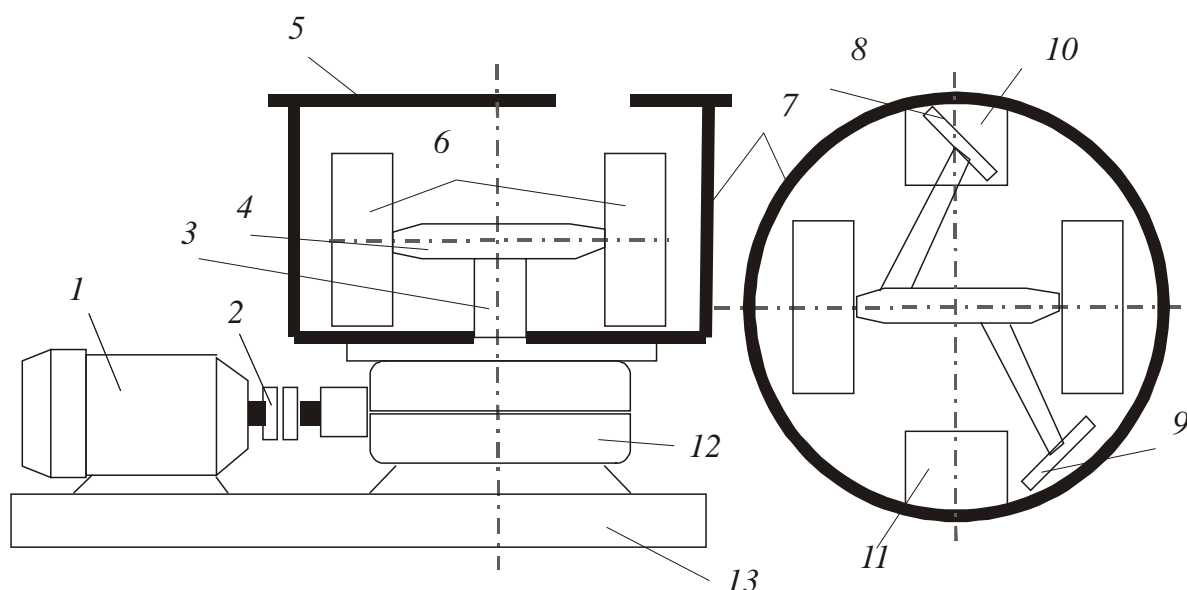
Схема конструкции бегунов: 1 – электродвигатель; 2 – муфта; 3 – консольный вал; 4 – траверса; 5 – крышка; 6 – катки; 7 – чаша; 8, 9 – отвалы; 10, 11 – разгрузочные люки; 12 – редуктор; 13 – станина
